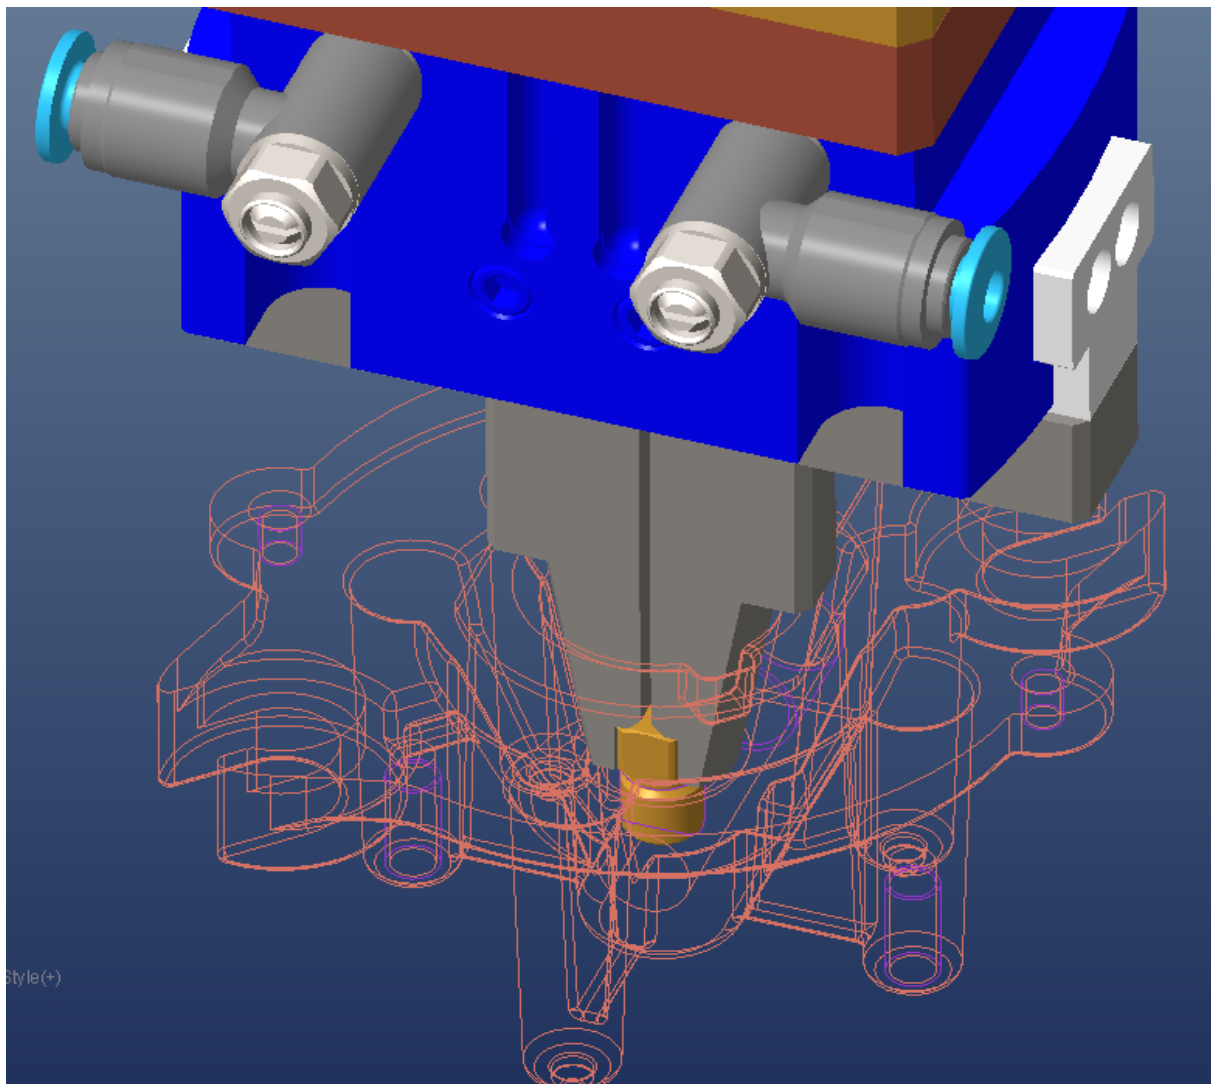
Manipulátor pro zašroubování trysek do hořáků
